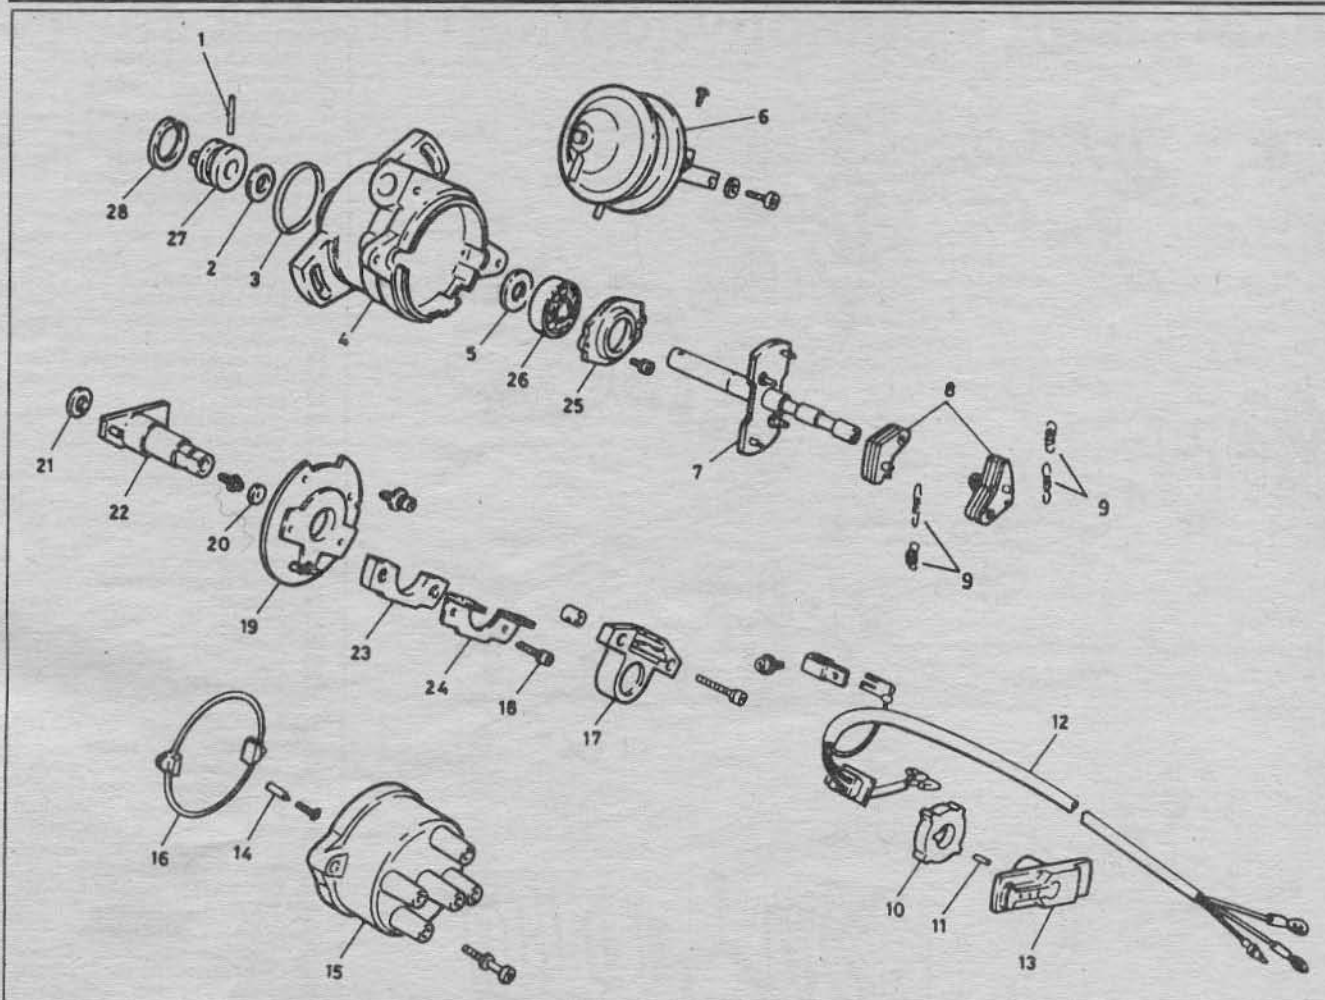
Распределитель НГАСН: 1 - штифт; 2 - упорная шайба; 3 - резиновое кольцо; 4 - корпус; 5 - сальник; 6 - диафрагма вакуумного регулятора; 7 - вал; 8 - грузы центробежного регулятора; 9 - пружина; 10 - магнитное сопротивление; 11 - штифт; 12 - первичный провод; 13 - ротор (бегунок); 14 - уплотнительный контакт; 15 - крышка; 16 - резиновое кольцо; 17 - датчик - прерыватель; 18 - винт; 19 - диск прерывателя; 20 - колпачок; 21 - упорная шайба; 22 - вал ротора; 23 - магнит; 24 - статор; 25 - упорная плата; 26 - подшипник; 27 - муфта; 28 - держатель.
